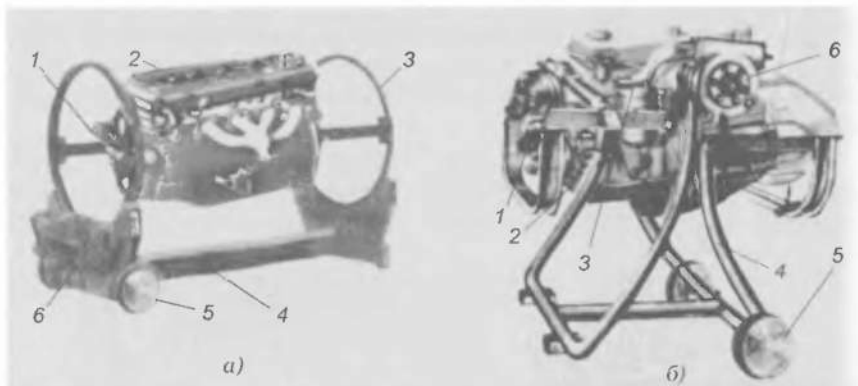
Стенды для разборки и сборки двигателей: *а* — поворотный вокруг продольной оси; *б* — поворотный вокруг поперечной оси; 1 — опора двигателя; 2 — двигатель; 3 — поворотная рукоятка; 4 — станина; 5 — колесо; 6 — механизм фиксированного поворота двигателя
